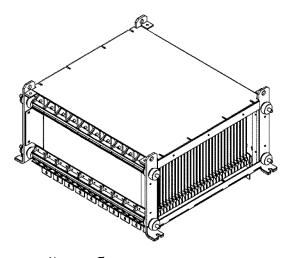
Внешний вид блока тормозных резисторов
